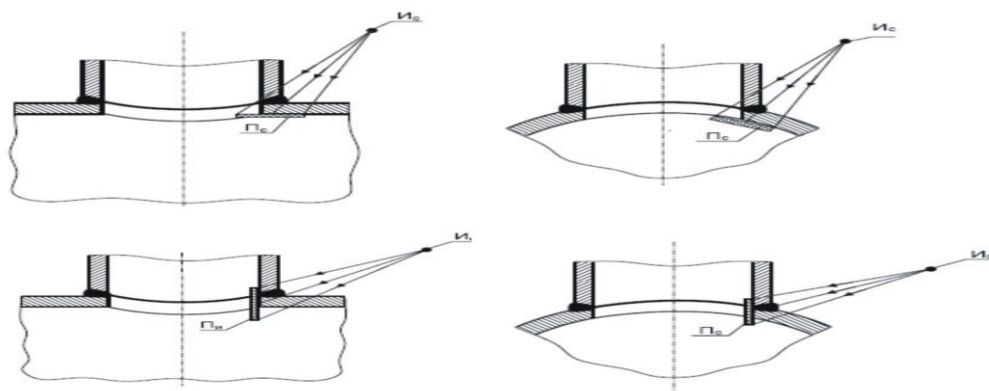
Схемы просвечивания криволинейных углового сварного соединения
